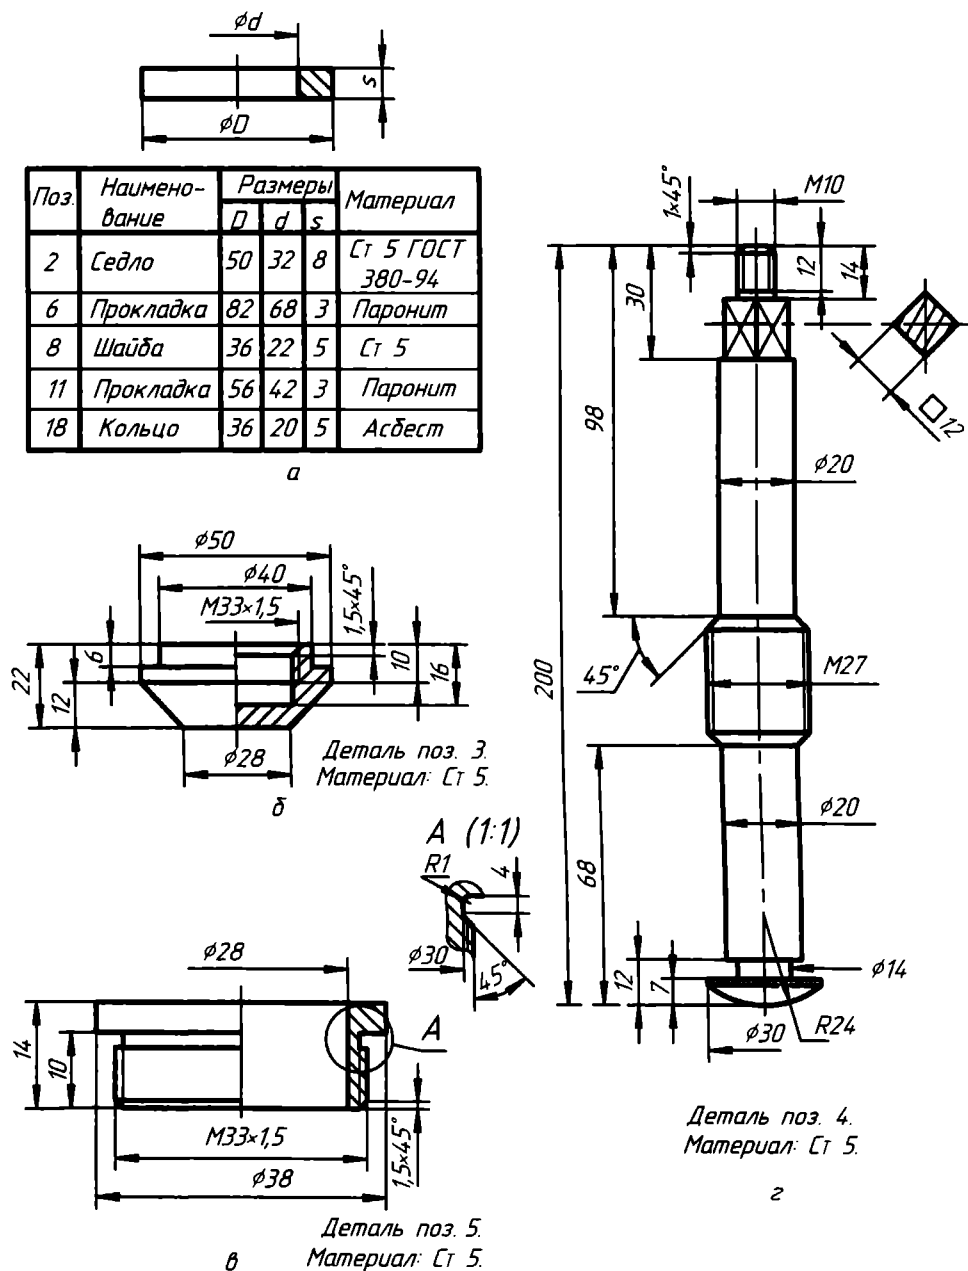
Чертежи: а — уплотнительных деталей; б — клапана; в — втулки; г — штока
